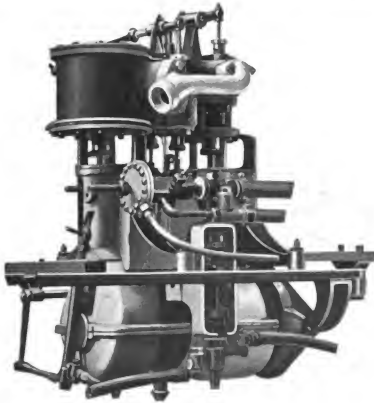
Dampfmotor der White Sewing Mach. Co. Cleveland.
